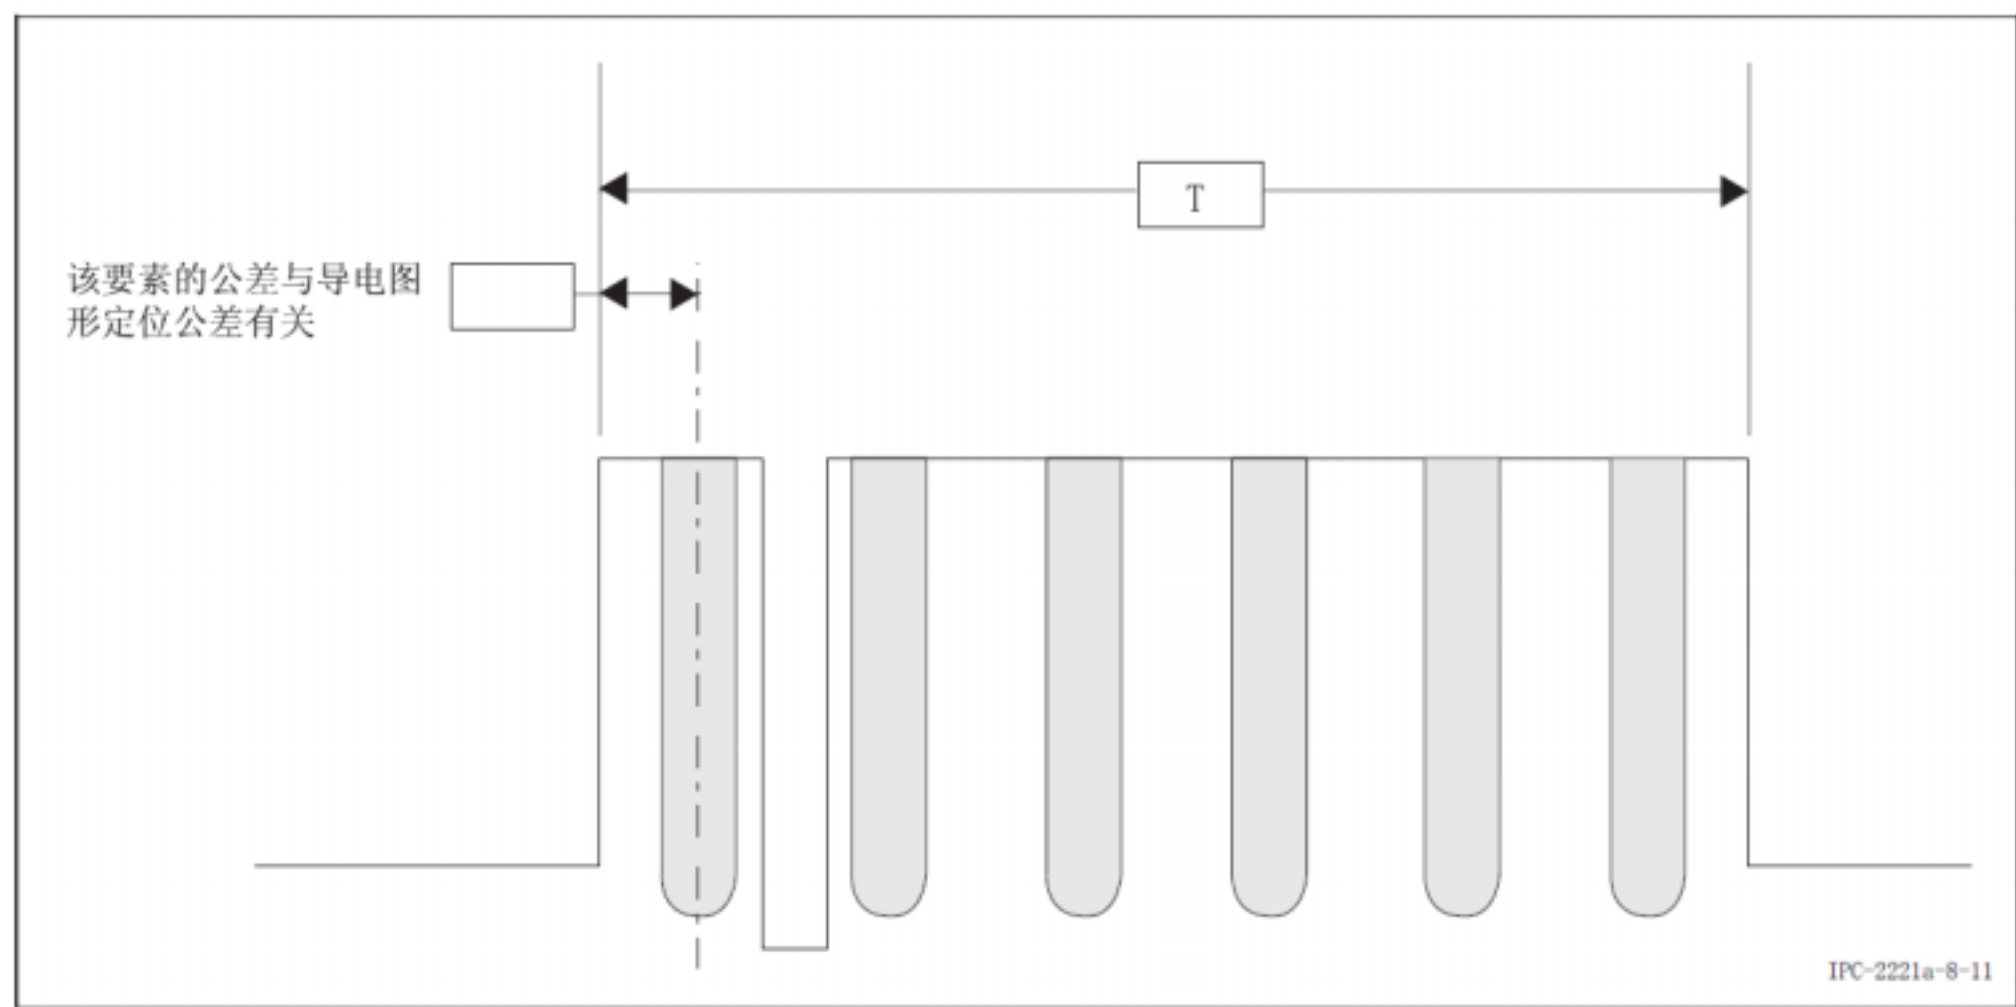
板边缘的公差（ IPC-2221A 图 8-11 板边缘的公差， P63）
